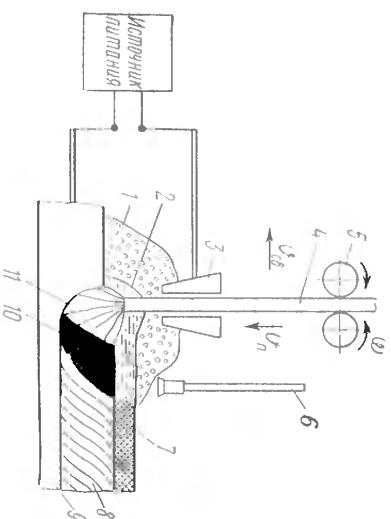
Схема дуговой сварки под флюсом:
